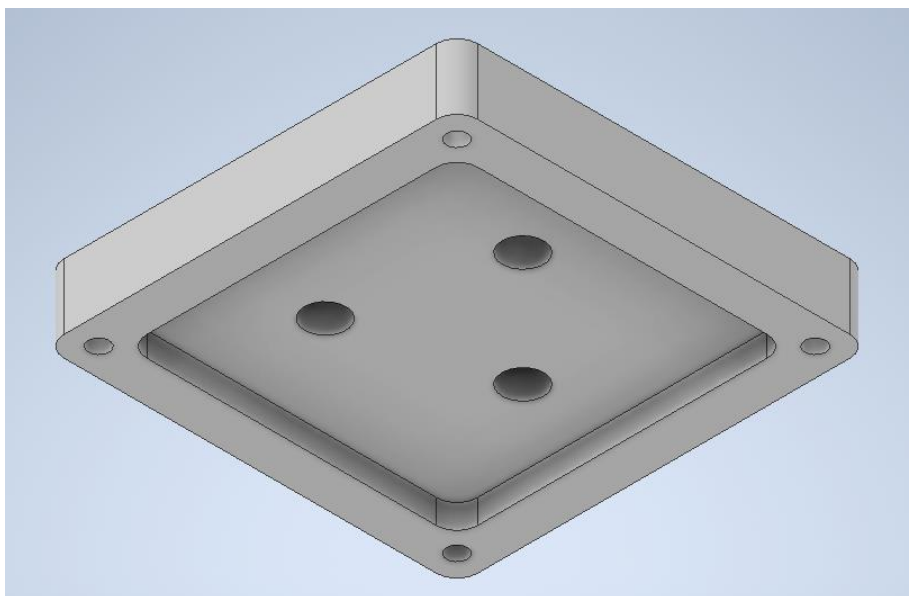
3Д модель крышки с отверстиями и углублениями под шестерни.
